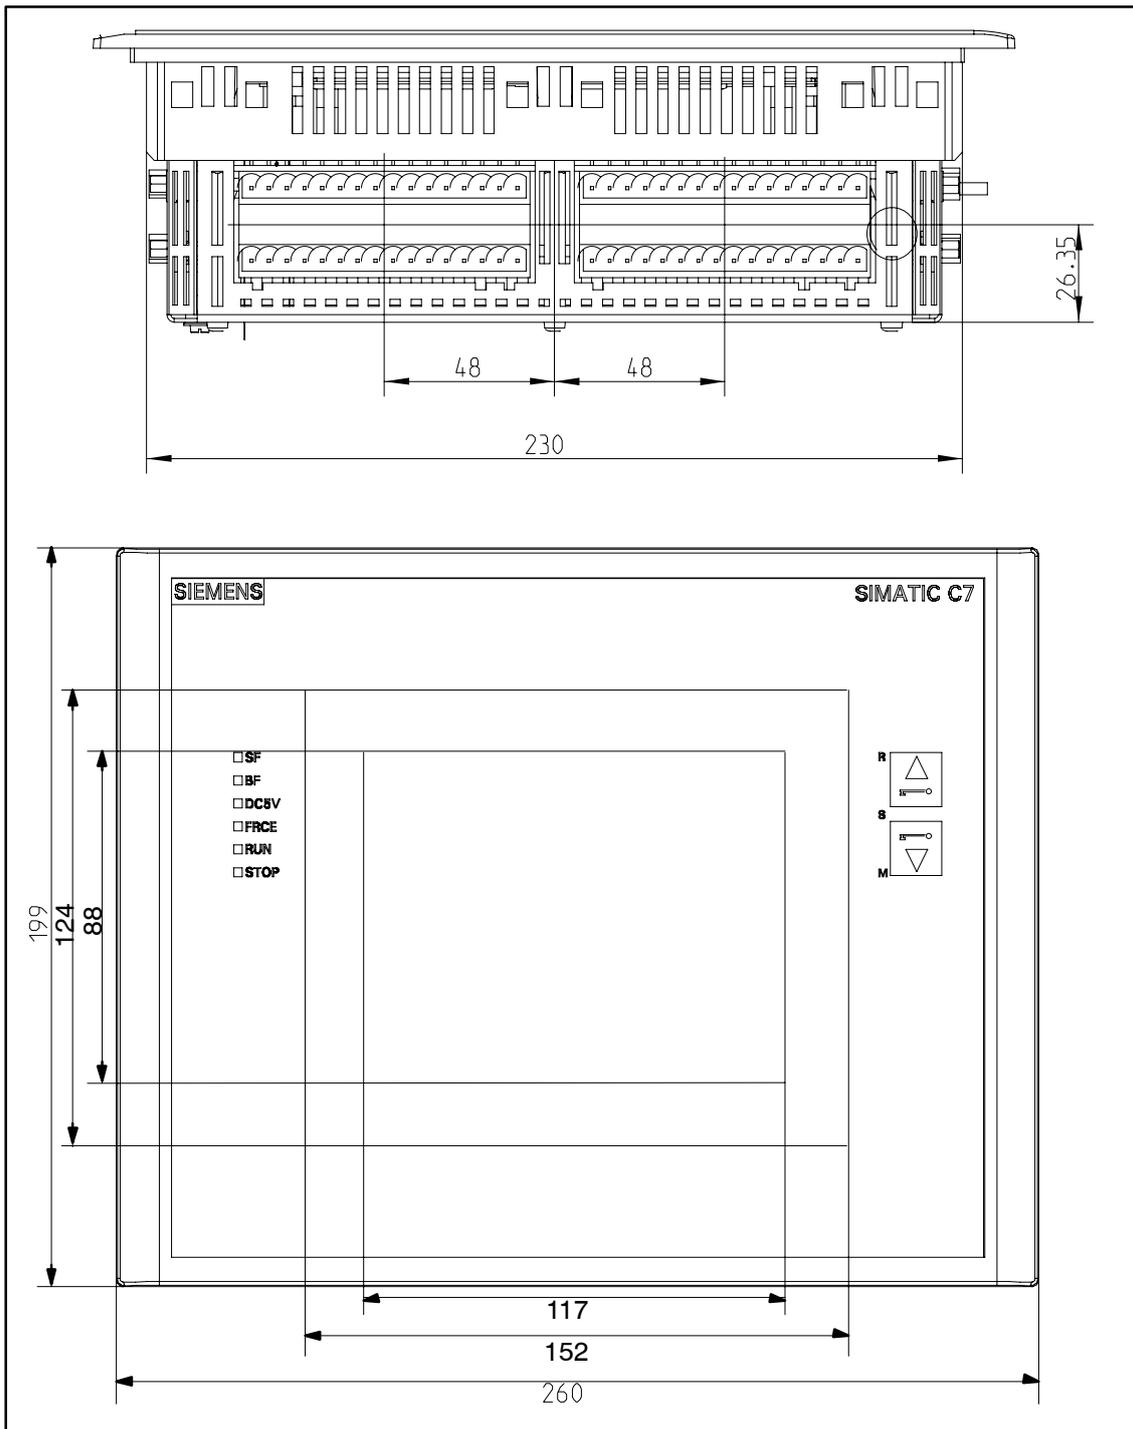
Maßbilder für das C7-635 Touch(Maße in Millimeter)
